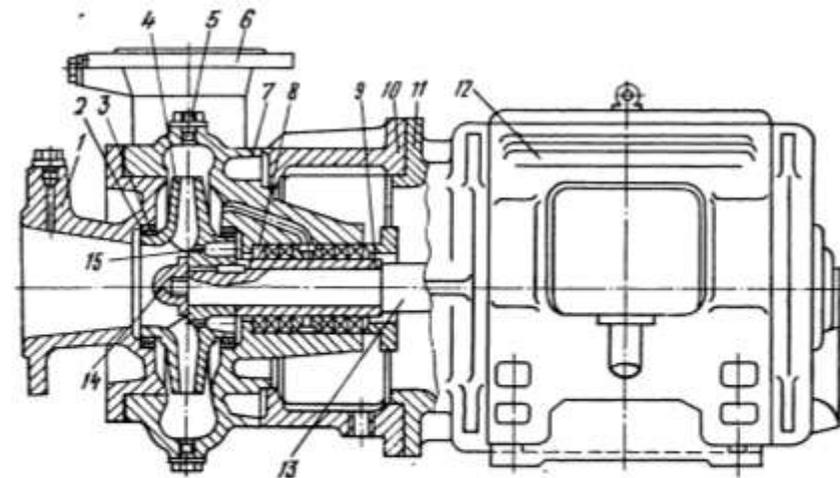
Конструкция моноблочного консольного центробежного насоса:
